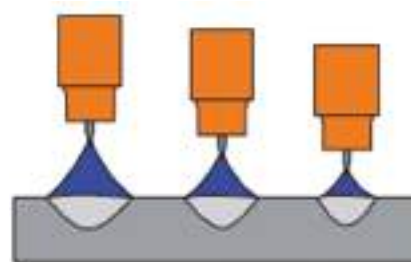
Penetração de soldadura em função da corrente de soldadura.
